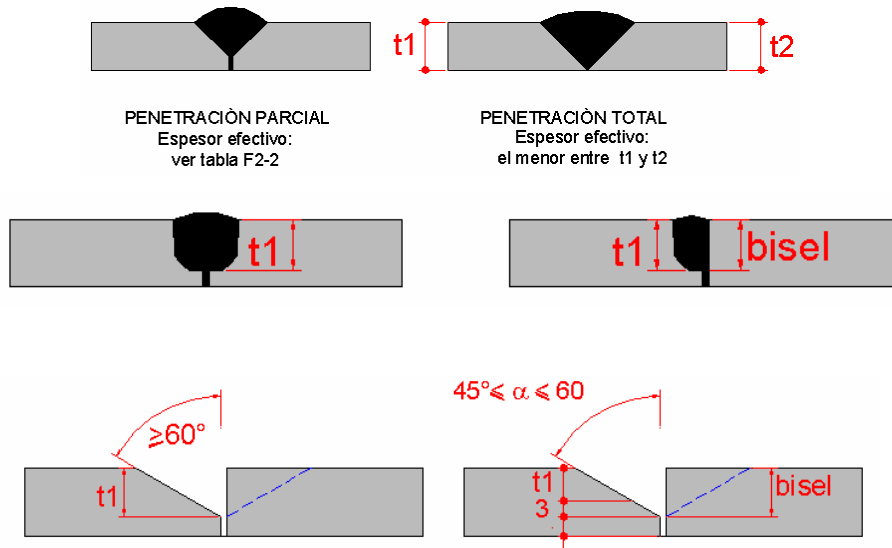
Detalle de soldaduras en acanaladas
